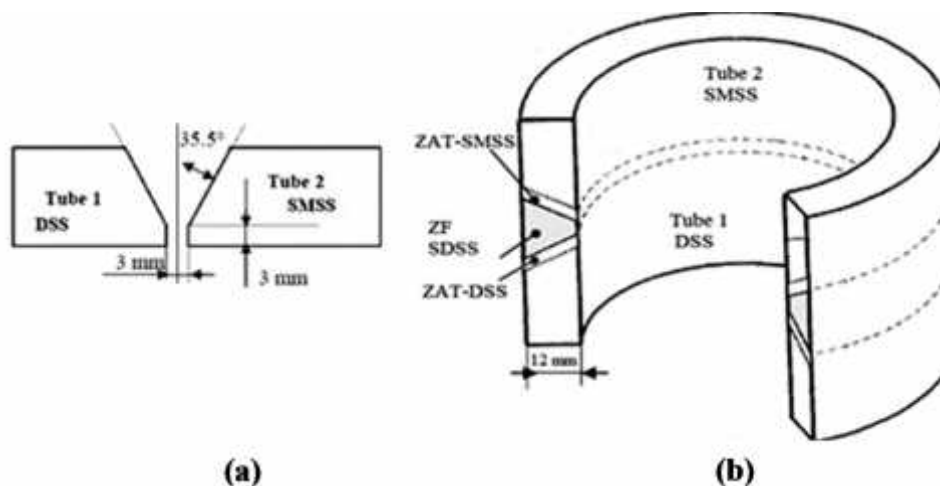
Schéma du chanfrein (a) et du tube soudé (b).
